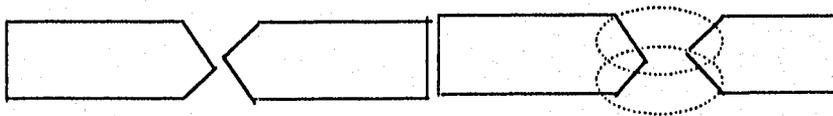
Efectuar la soldadura en placas colocadas a tope con preparación en doble "V"
